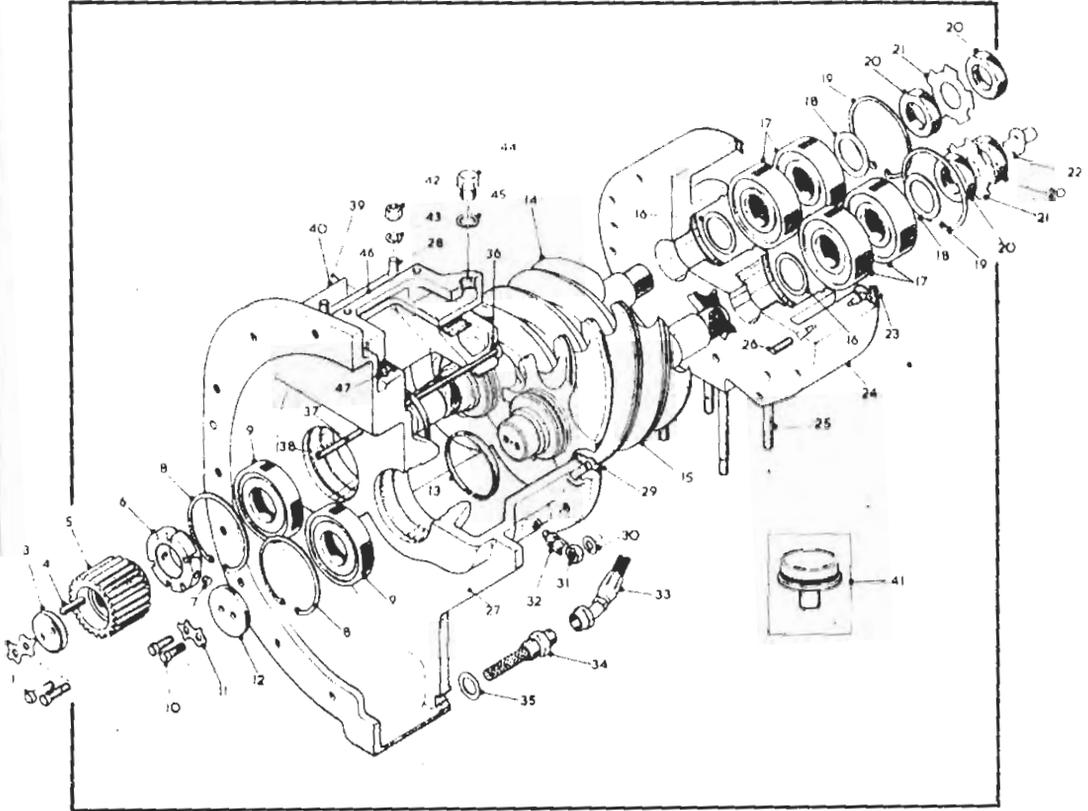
Despiece de un compresor rotativo de tornillo (HOLMAN). 1.- Tornillo. 2.- Placa del freno. 3.- Retenedor. 4.- Chaveta. 5.- Piñón. 6.- Tuerca. 7.- Pivote. 8.- Frenillo. 9.- Rodamiento. 10.- Tornillo. 11.- Placa de freno. 12.- Retenedor. 13.- Anillo. 14.- Rotor (macho). 15.- Rotor (hembra). 16.- Disco. 17.- Rodamiento. 18.- Arandela. 19.- Frenillo. 20.- Tuerca. 21.- Placa de freno. 22.- Irinquete. 23.- Junta. 24.- Carcasa. 25.- Espárrago. 26.- Pasador. 27.- Carcasa. 28.- Espárrago. 29.- Junta. 30.- Arandela. 31.- Tuerca. 32.- Racor. 33.- Manguera. 34.- Filtro. 35.- Arandela. 36.- Espiga. 37.- Engrasador. 38.- Prisionero. 39.- Tornillo. 40.- Placa de fabricante. 41.- Filtro. 42.- Tuerca. 43.- Arandela. 44.- Tapón. 45.- Arandela de fibra. 46.- Adaptador. 47.- Junta.
